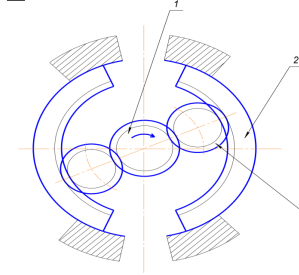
Планетарний процес наочування: 1 – нерухомі сегменти; 2 - обертвий різьбовий ролик; 3 – деталі, що обробляються
